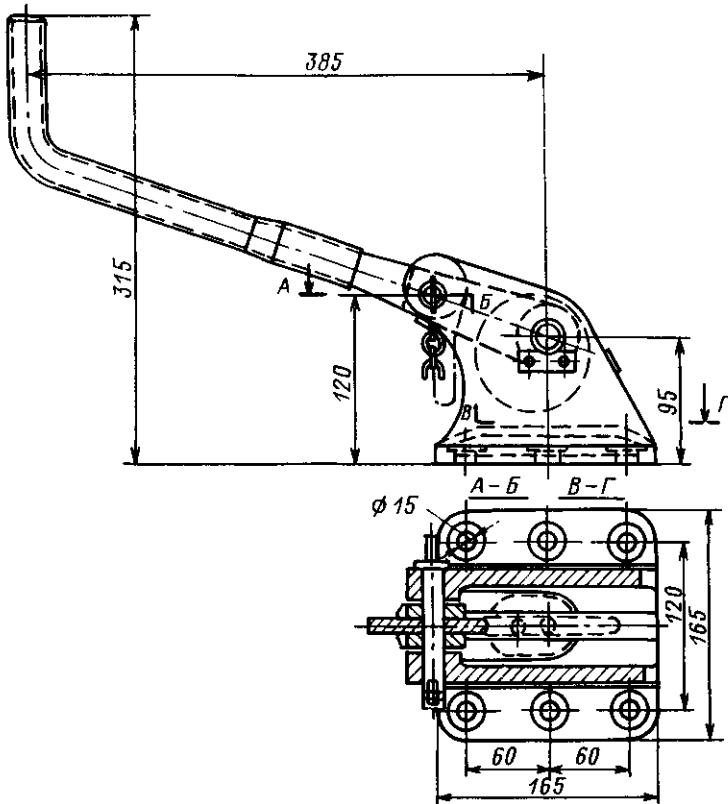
Эксцентриковый стопор для цепи калибром 11–13 мм
